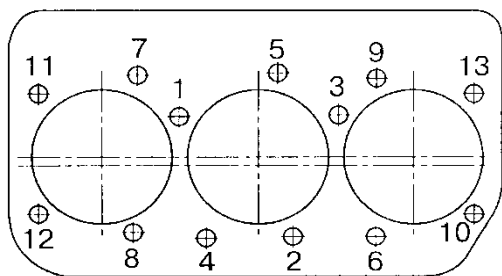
Схема затяжки болтов головок цилиндров двигателя
